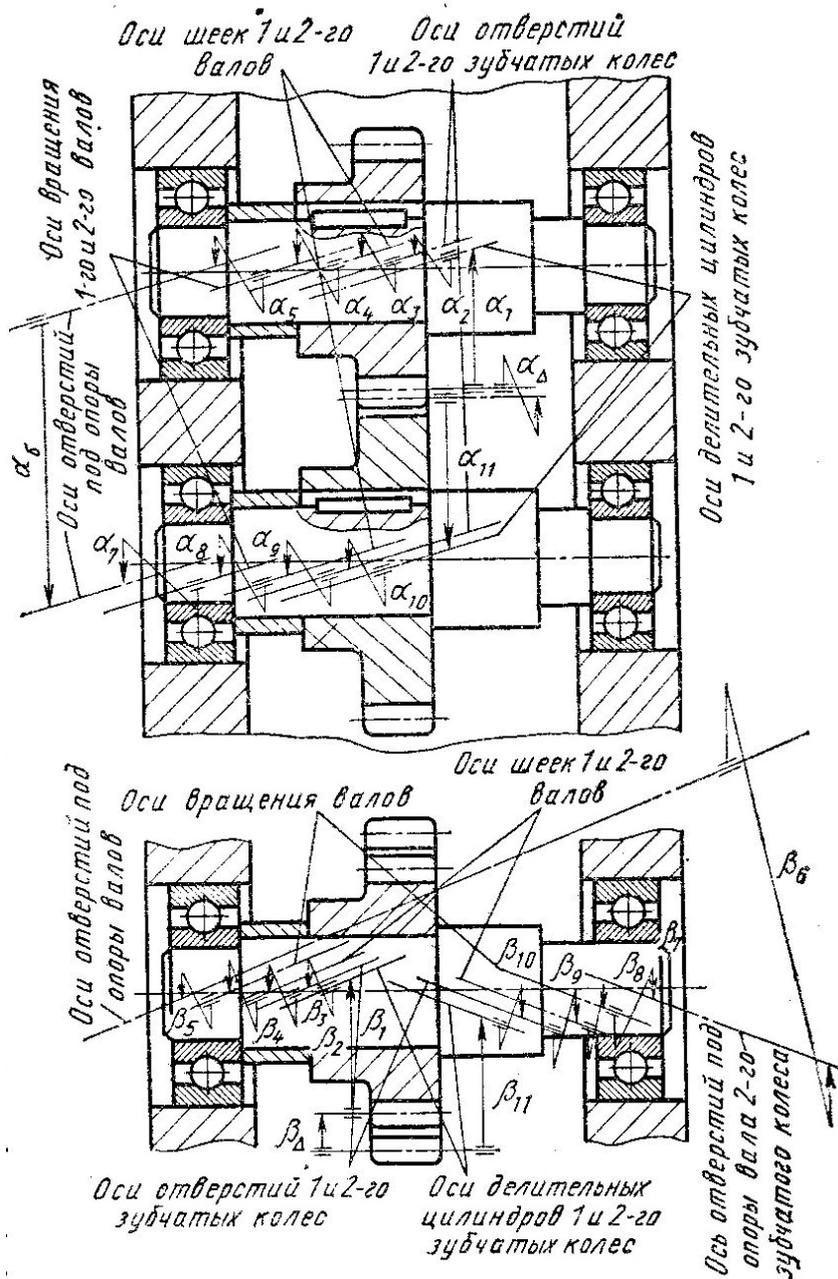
Схемы размерных цепей, определяющих точность относительного поворота образующих рабочих поверхностей зубьев цилиндрических зубчатых колес в двух координатных плоскостях
